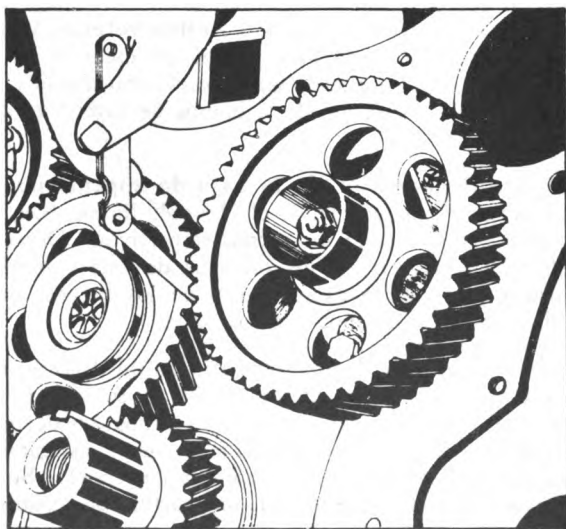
Revisión de la luz entre dientes de engranajes.
